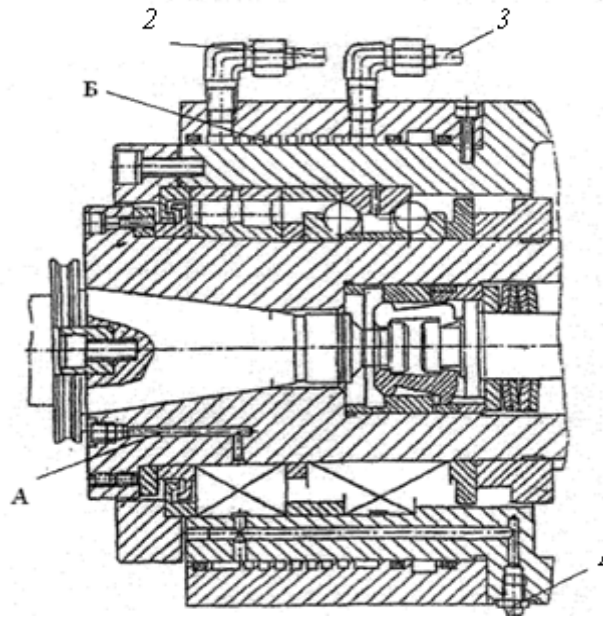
Шпиндельный узел многоцелевого фрезерно-сверлильно-расточного станка
